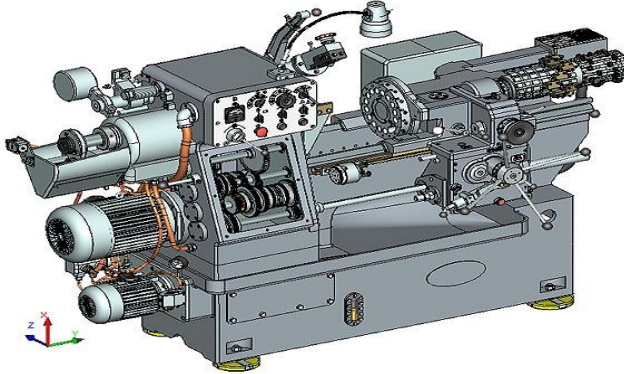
Токарно-револьверний верстат з горизонтальною віссю обертання (паралельно осі верстата)
